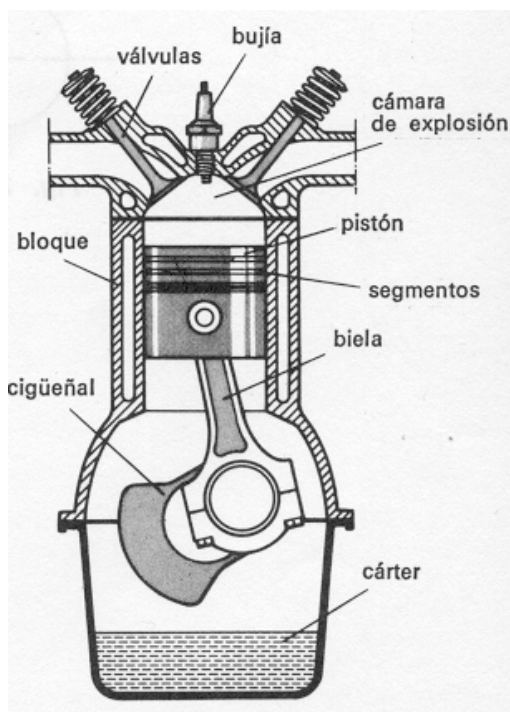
Partes de un cilindro de un motor de combustión interna. Fuente: <https://ingemecanica.com/>
